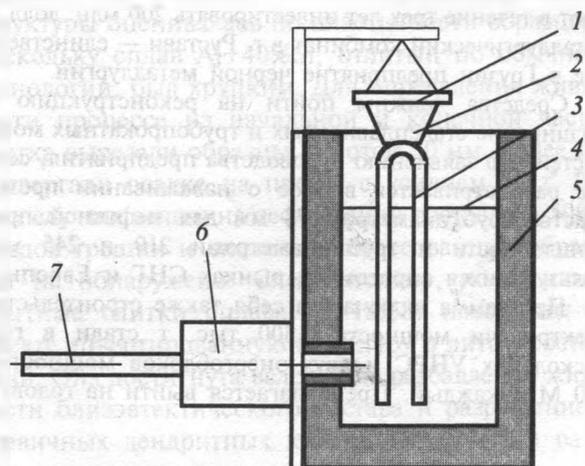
Схема обработки расплава ультразвуком: 1 — преобразователь; 2 — концентратор; 3 — излучатель; 4 — уровень металла; 5 — металлоприемник; 6 — кристаллизатор; 7 — отливка
